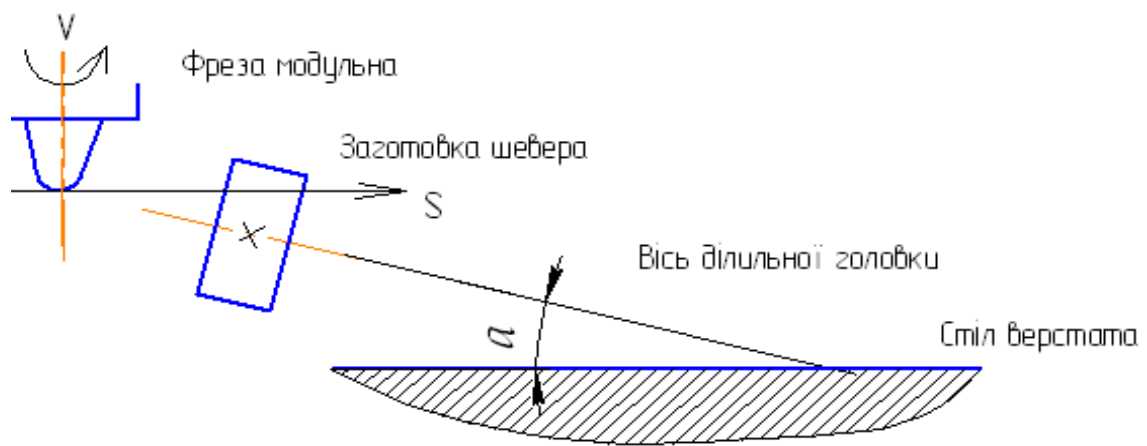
Фрезерування на горизонтально-фрезерному верстаті за допомогою ділильної головки
